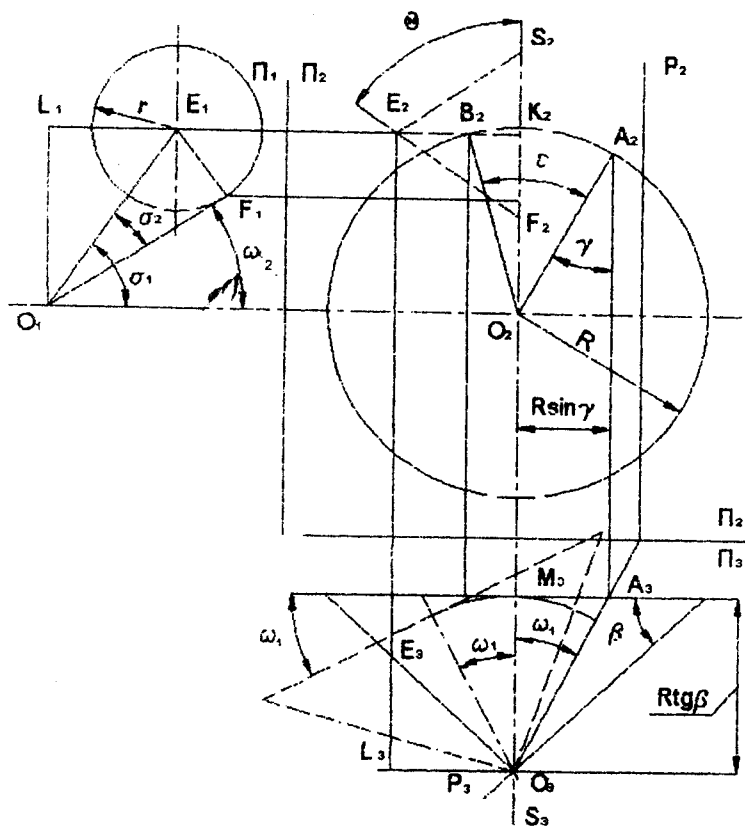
Визначення кутів установки заготовки при фрезеруванні зубців на конічній поверхні
